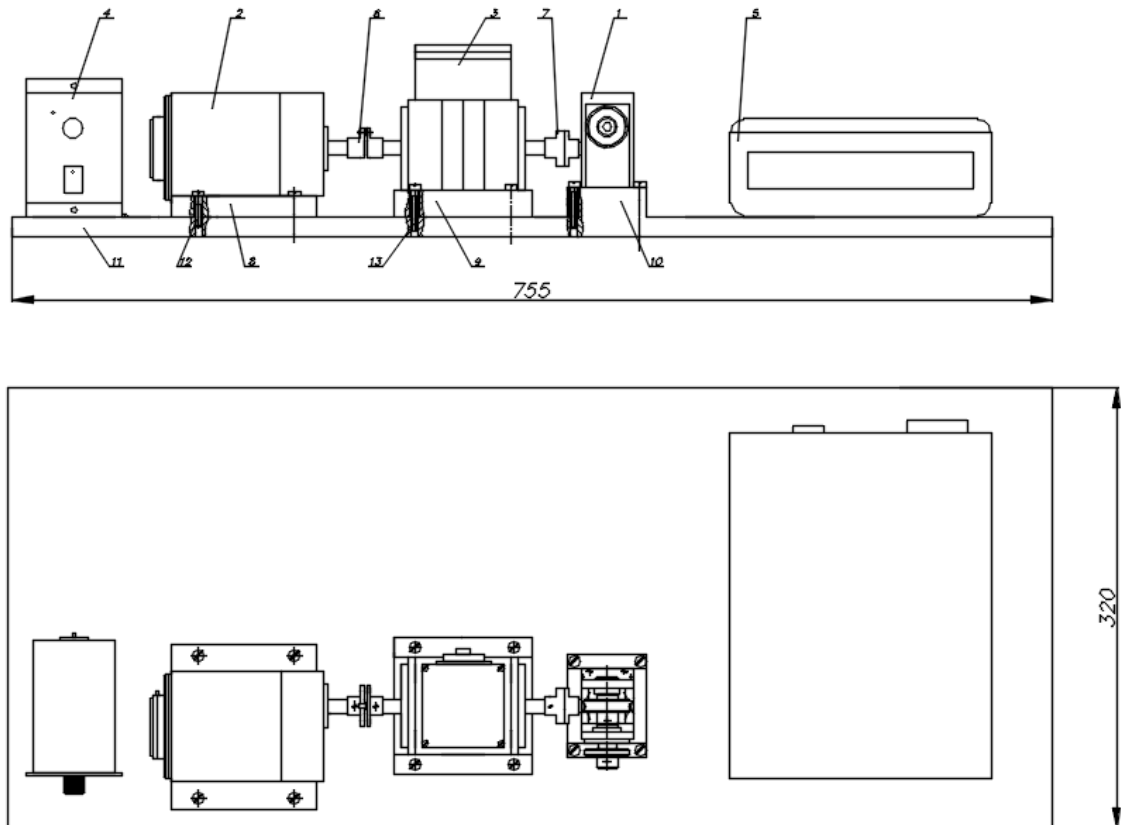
Ескіз станда для обкатки та контролю крутного моменту редуктора.
